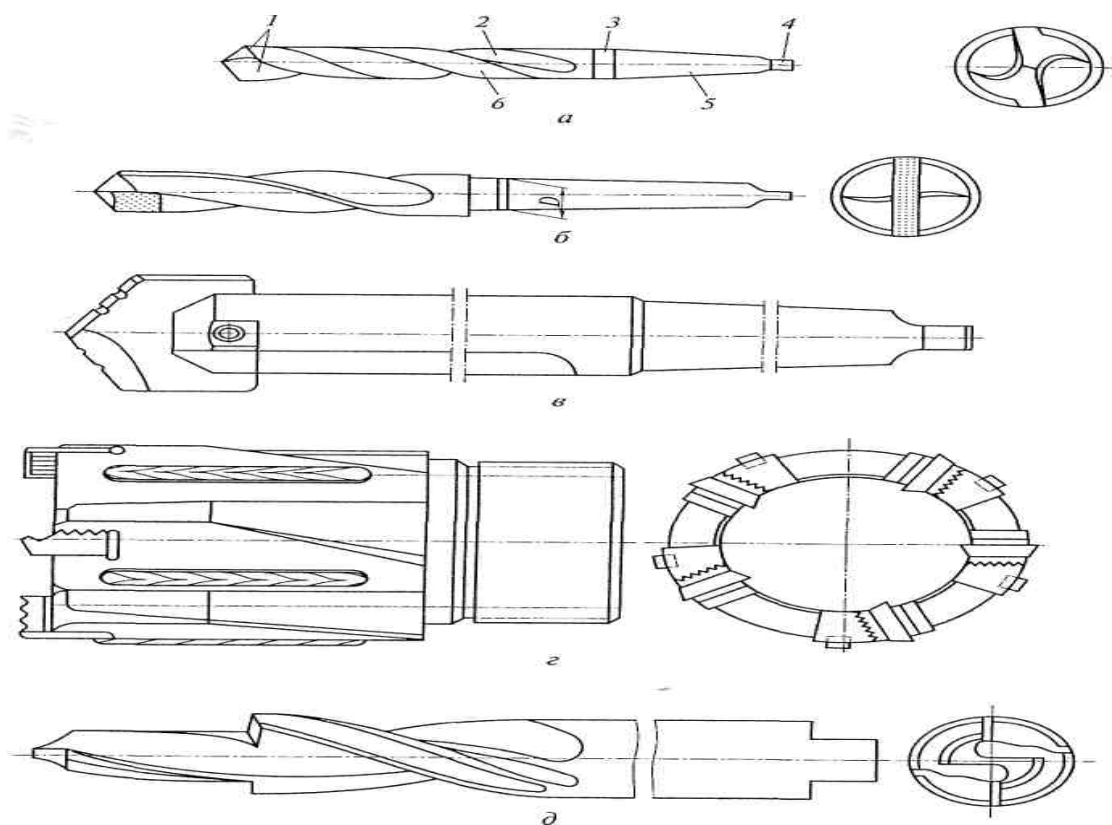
Сверла: *a* — цилиндрическое с винтовой канавкой и коническим хвостовиком: 1 — режущая часть; 2 — спиральная канавка; 3 — шейка; 4 — лапка; 5 — хвостовик; *б* — рабочая часть; *б* — цилиндрическое с пластиной из твердого сплава; *D* — диаметр хвостовика; *в* — перовое для глубоких отверстий; *г* — полое для кольцевого сверления отверстий; *д* — ступенчатое Удлиненные сверла больше стандартных на 30...40 %.
